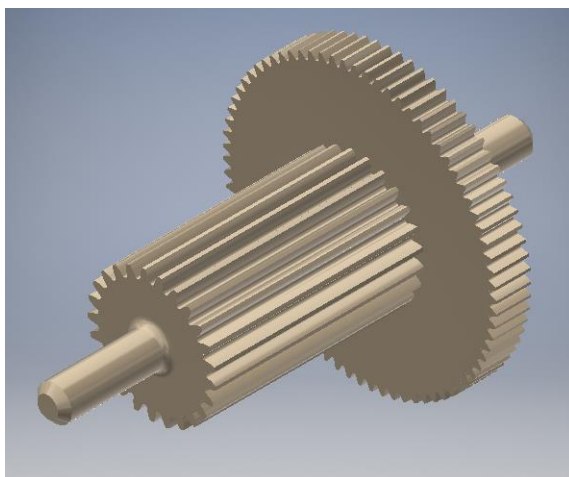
Зубчатое колесо и шестерня 2 с ободом колеса
